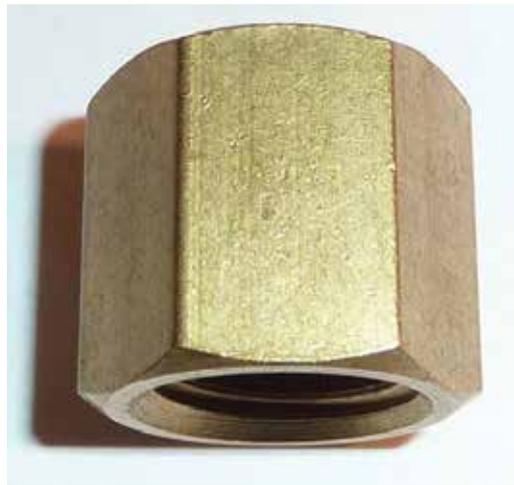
Tampa sextavada com gaxeta de borracha/elastômero.
